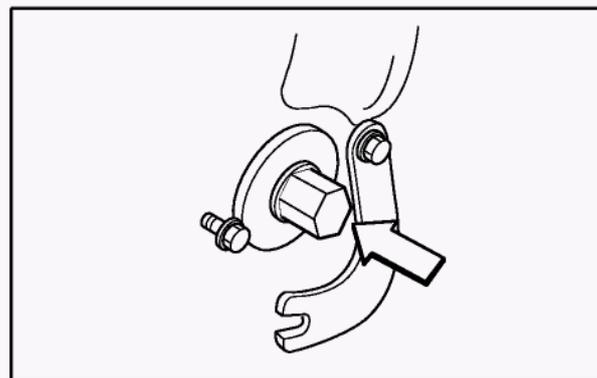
Положение валоповоротного устройства (Вал задвинут)
